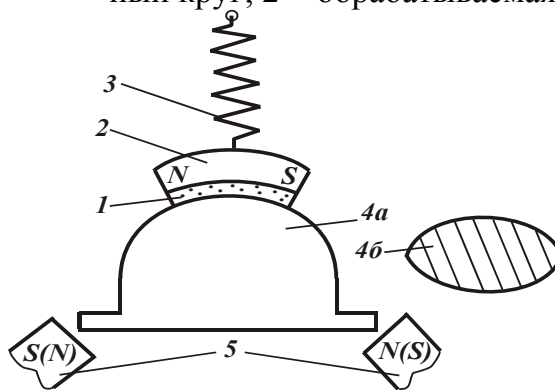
Маятниковая схема электроискрового магнито-импульсного шлифования выпуклых сферических поверхностей: 1 – шлифовальный инструмент; 2 – патрон для шлифовального инструмента из намагниченного материала или с электромагнитом; 3 – пружина подвески патрона со шлифовальным инструментом; 4 – обрабатываемая деталь; 4а – полусферический вал, 4б – сферический вал; 5 – электромагниты.
